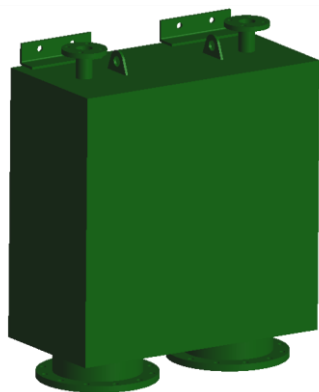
Вертикальный МД и устройство РПН с НБОМГ
